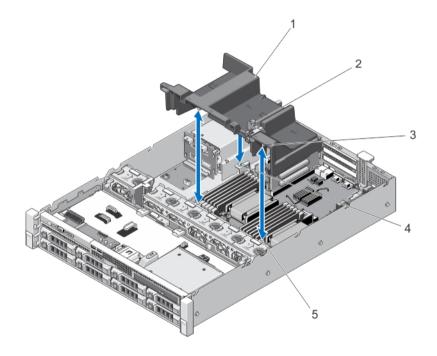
Extracción e instalación de la cubierta de refrigeración
